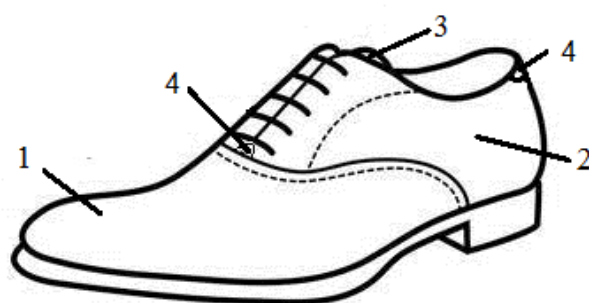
Наружные детали заготовки полуботинка:
